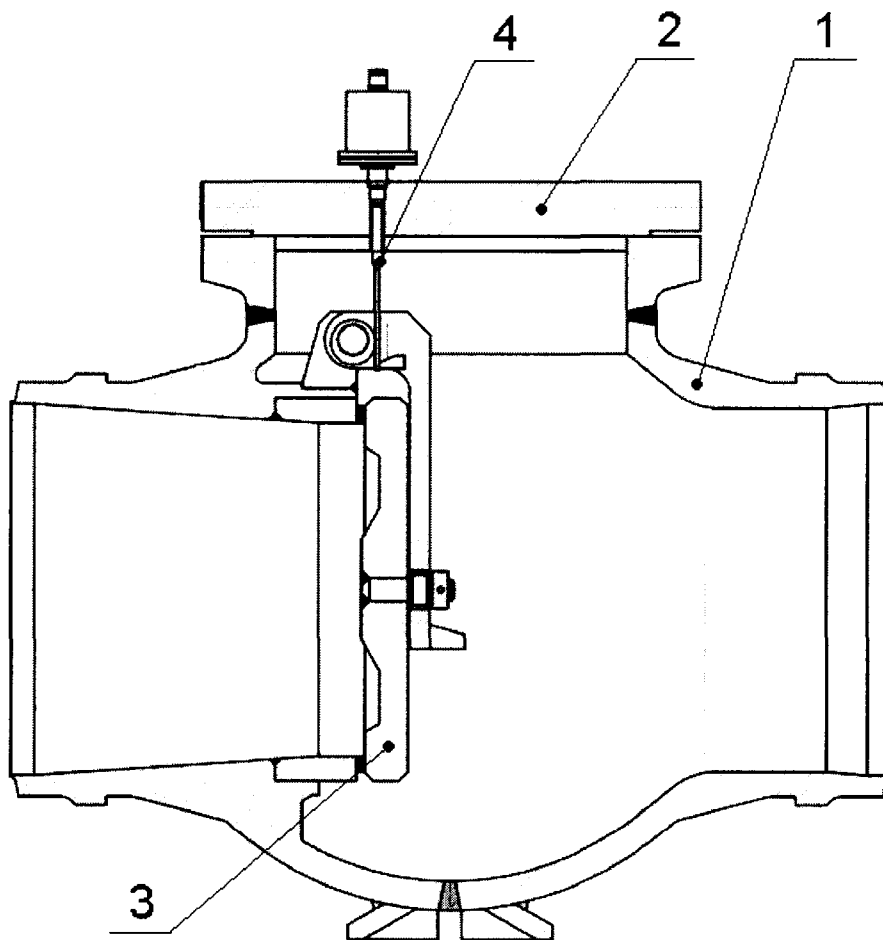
Клапан типа A42127-4160/300-600L в сборе
